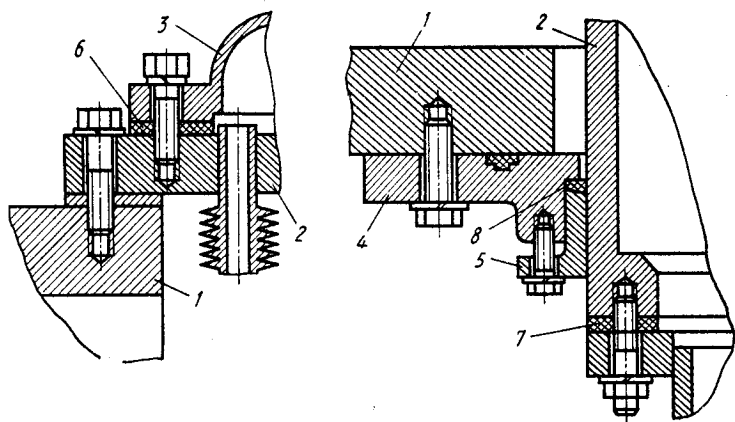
Крепление газоохладителя к корпусу статора турбогенератора ТВВ:
